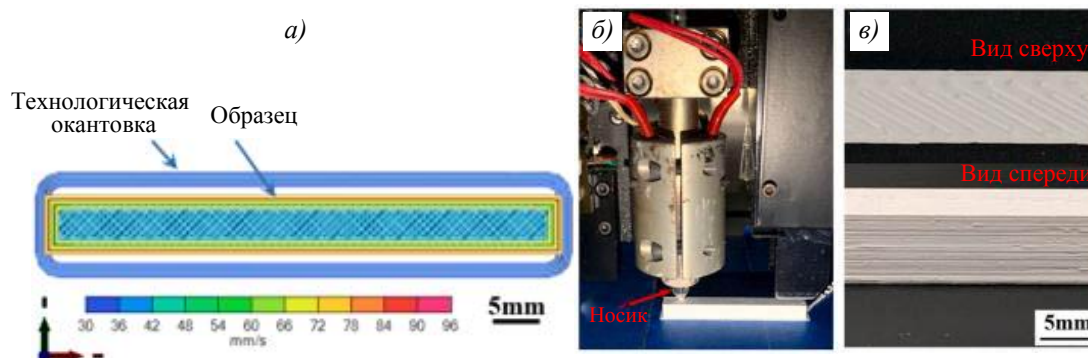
3D-печать образца ZrO_2 : а – разделение 3D-модели на слои; б – процесс печати; в – полученный образец
